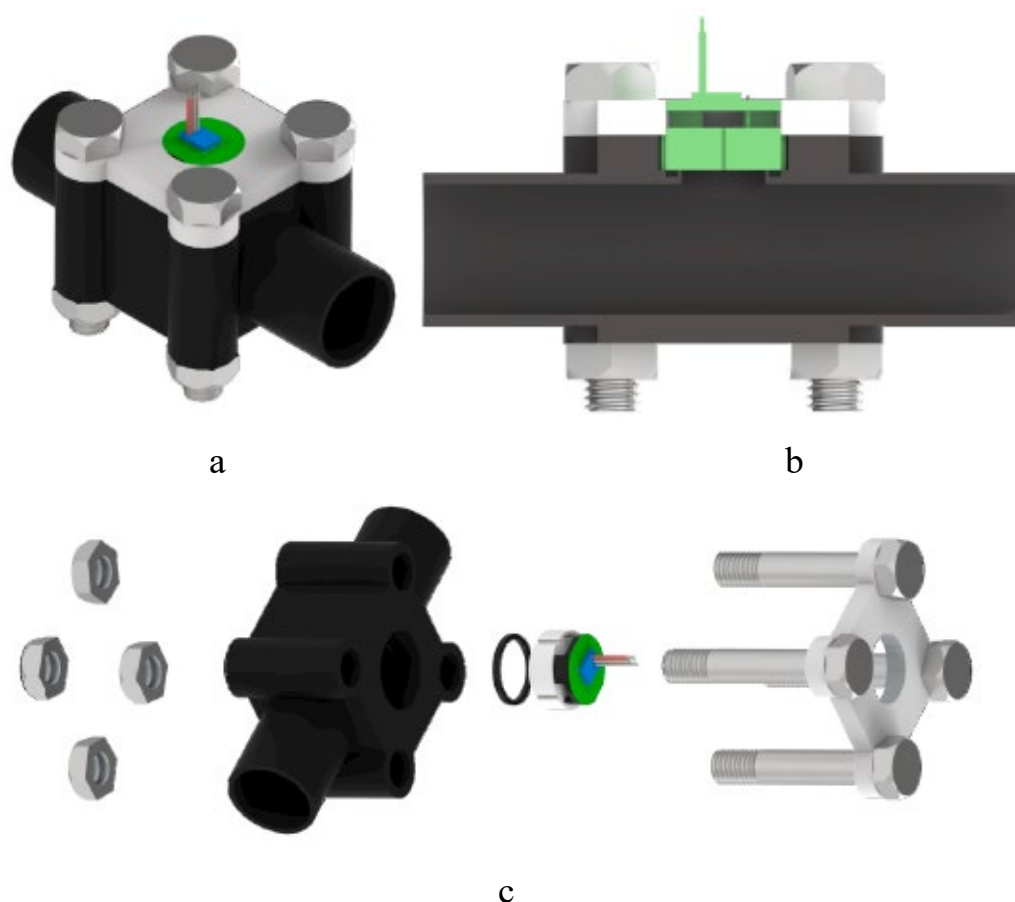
Зібраний CAD-проект корпусу датчика
